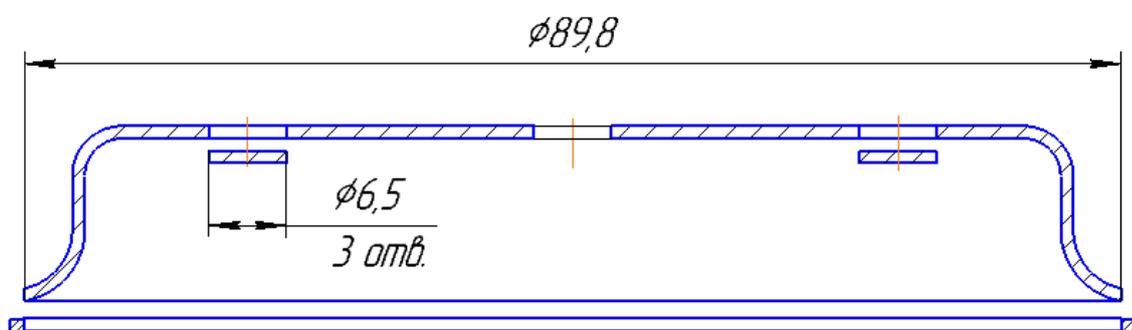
Обрезка фланца и пробивка отверстий
